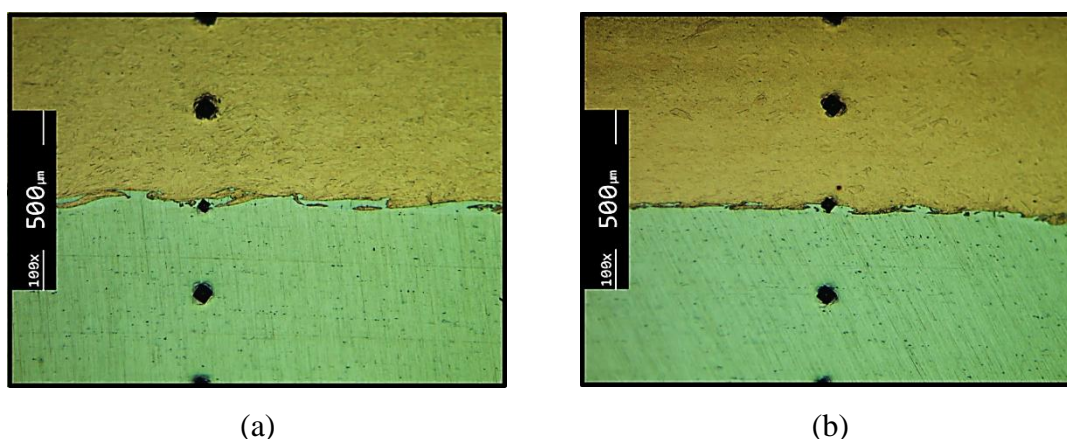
Indentações na soldadura SE1: (a) SE1_25_2; (b) SE1_15_5
